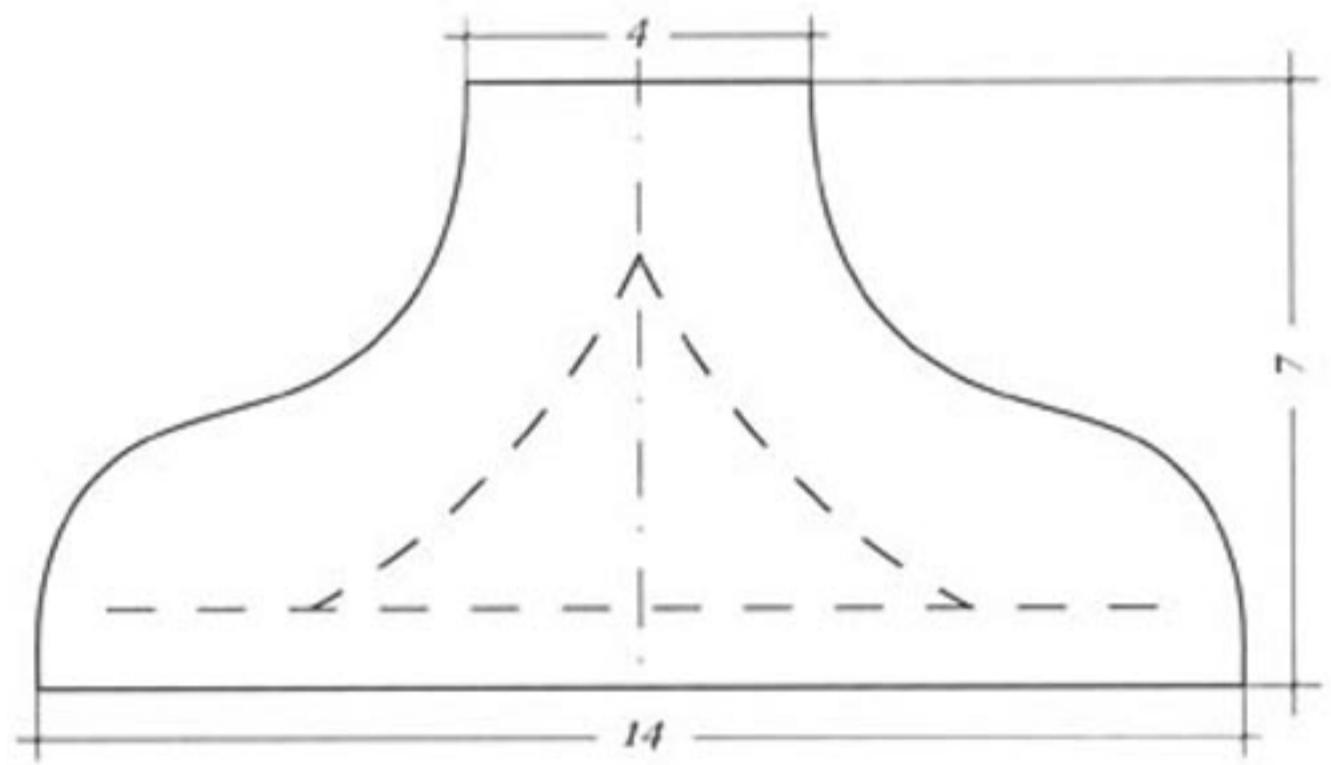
Чертеж и схема разметки основания двухсвечника к рис. 175
